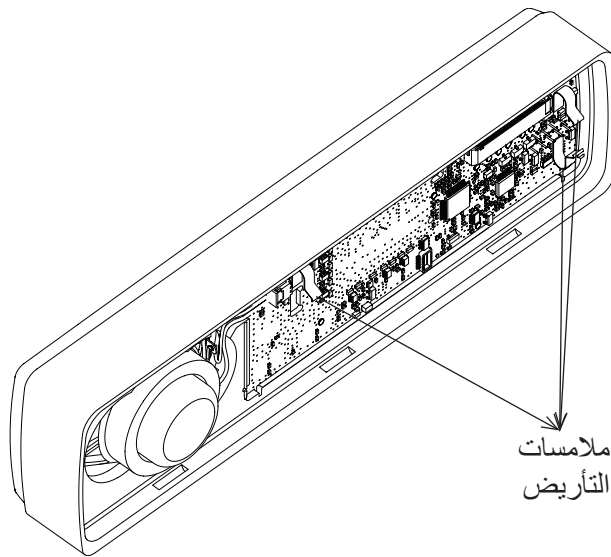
تركيب لوحة PCB في لوحة المفاتيح
